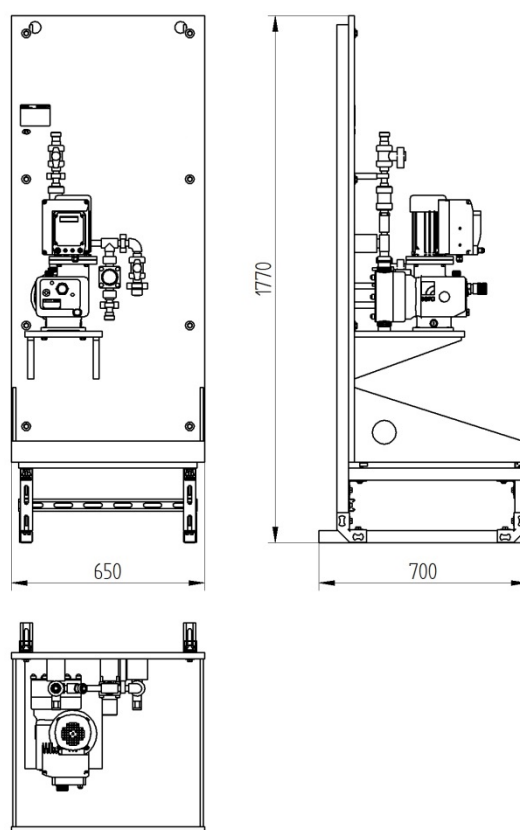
Dimensions CVD 1 (montage au sol, châssis acier)
